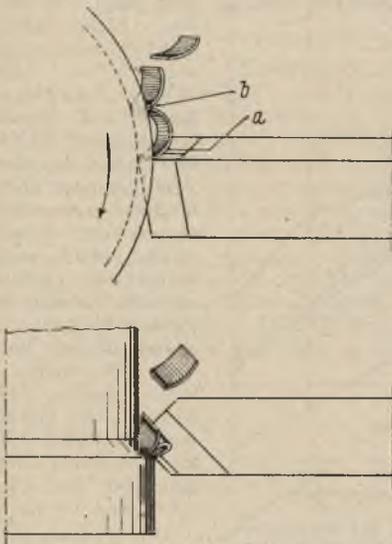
Drehstahlhalter mit verstellbarem Spanbrecher.
